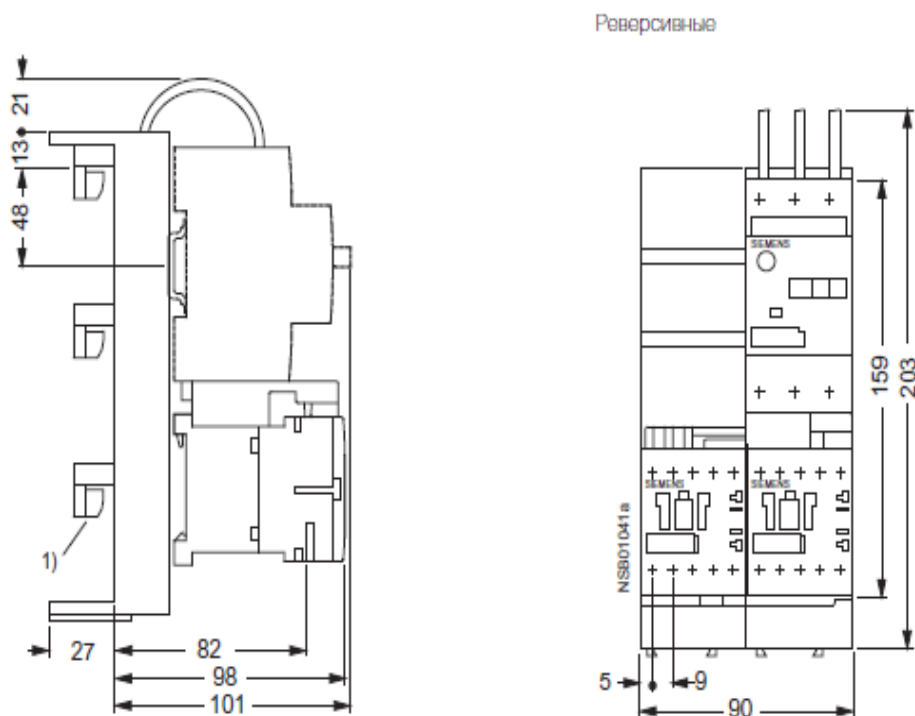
Типоразмер фидерной сборки 3RA12.
